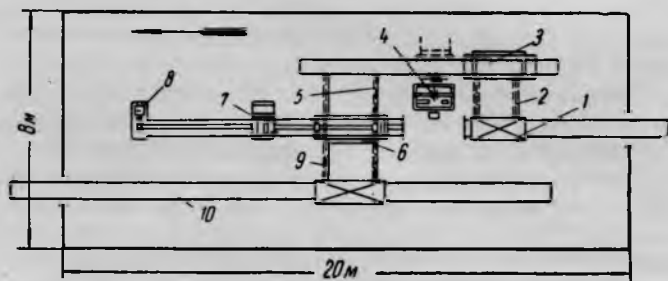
Схема размещения шпалорезного и шпалооправочного станков:
